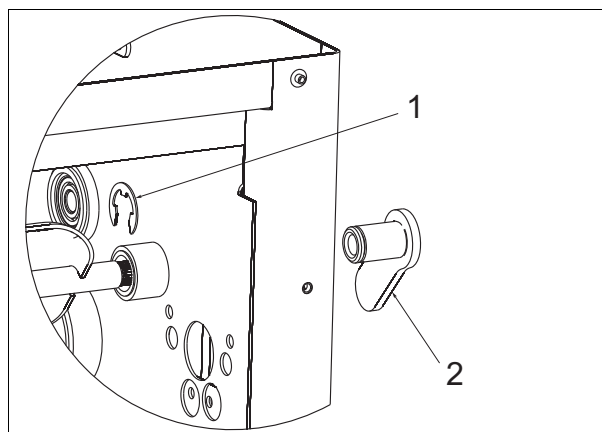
Retrait de l'assemblage des leviers 300 et 600
